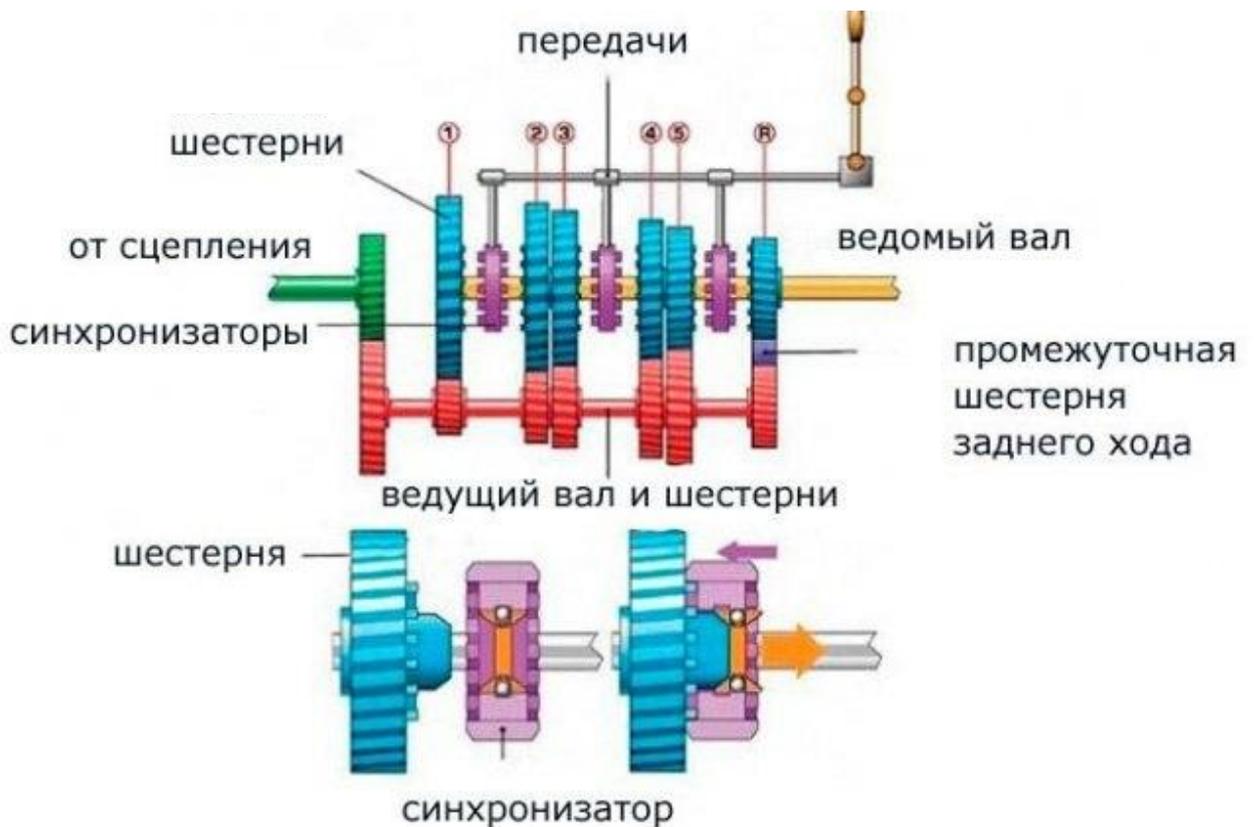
Конструктивная схема пятиступенчатой коробки передач
